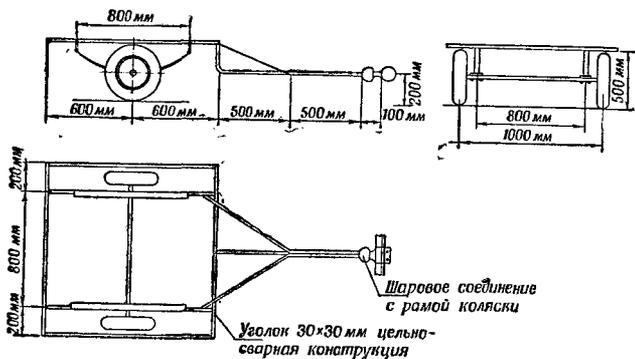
Рама одноосного прицепа с колесами мотороллера
